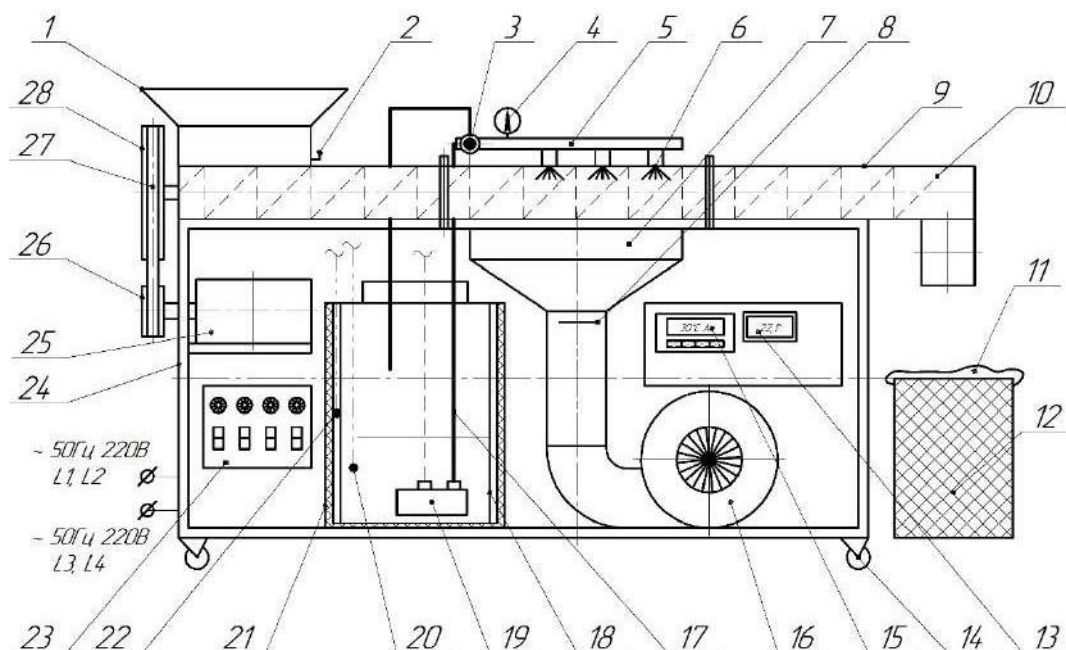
Конструктивно-технологічна схема установки для обробки насіння біопрепаратами: 1 – завантажувальний лоток; 2 – заслінка регулювання подачі насіння; 3 – регулятор тиску рідини; 4 – манометр; 5 – труба подачі рідини; 6 – форсунка з розпилювачем; 7 – повітропровід; 8 – заслінка регулювання подачі повітря; 9 – корпус шнека (3 частини); 10 – шнек; 11 – мішок; 12 – кошик для мішка; 13 – показчик температури рідини; 14 – колесо; 15 – регулятор температури; 16 – вентилятор; 17 – трубопровід подачі рідини; 18 – бак робочої рідини; 19 – мембранний насос; 20 – датчик температури рідини; 21 – нагрівальний елемент; 22 – датчик температури нагрівального елемента; 23 – блок керування (шнек, насос, нагрівання рідини, вентилятор); 24 – рама; 25 – електродвигун; 26 – шків електродвигуна; 27 – пас; 28 – шків шнека
